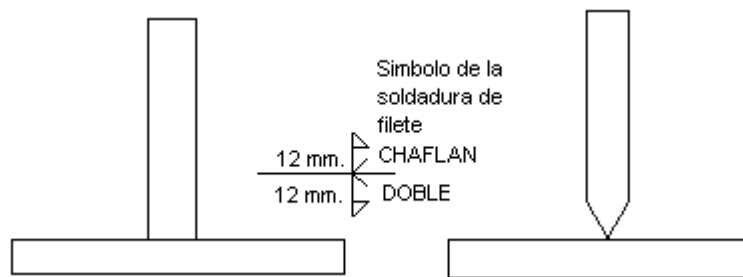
Aplicación de combinación de símbolos de soldadura
